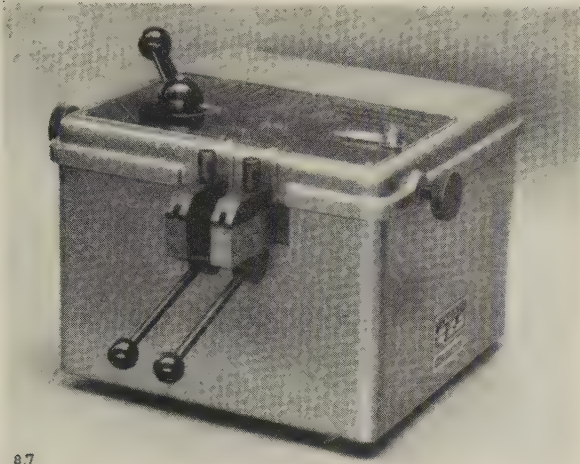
Stumpfschweißgerät für Litzen.
